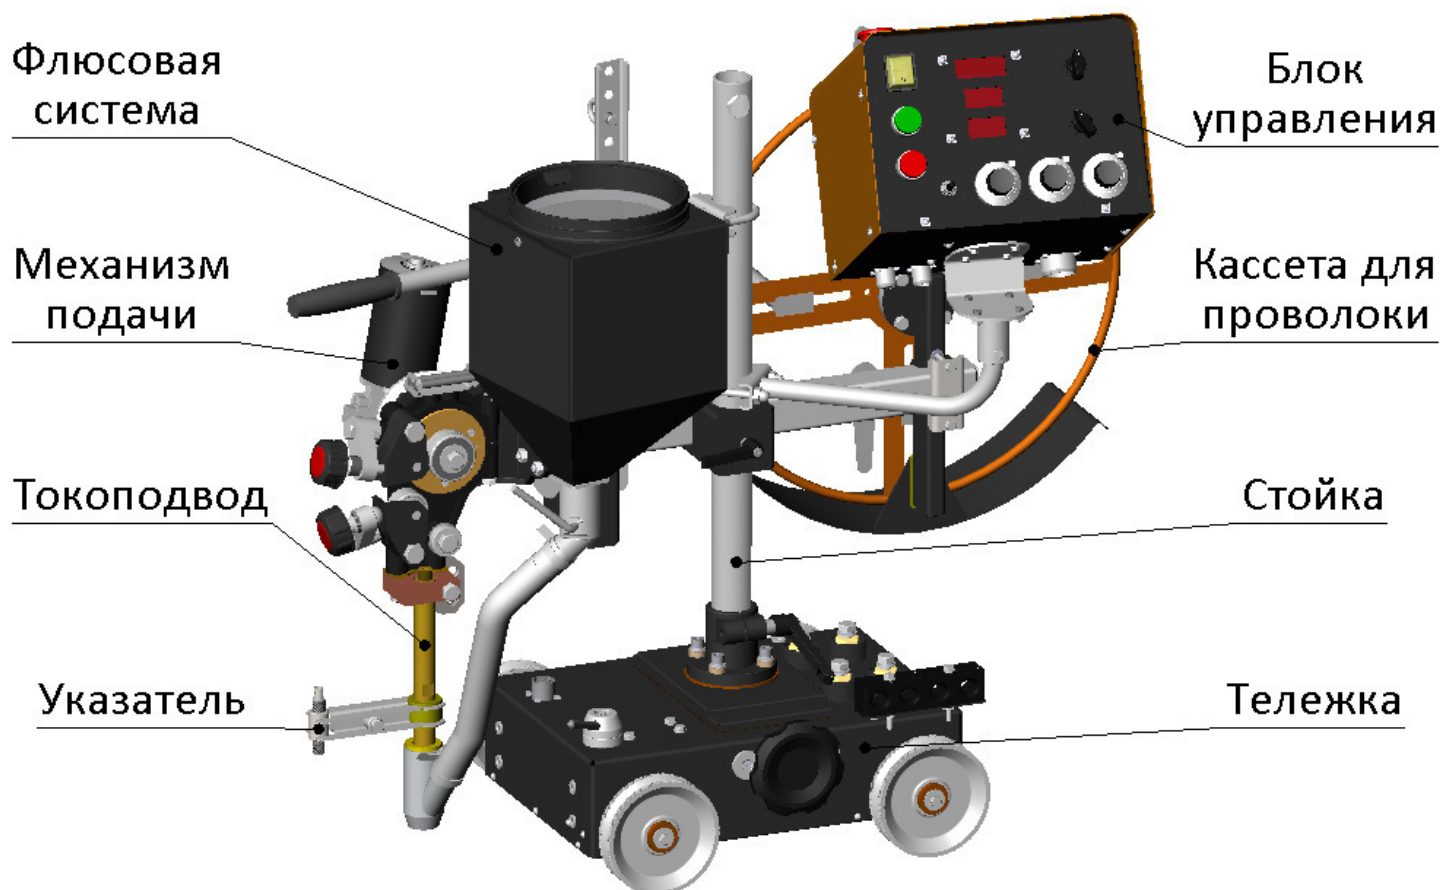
Автомат для сварки SAW, базовое исполнение.
